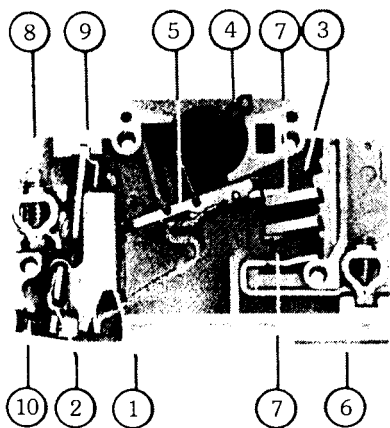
Vista interna do minidisjuntor 5 SM. Cortesia: Siemens.
